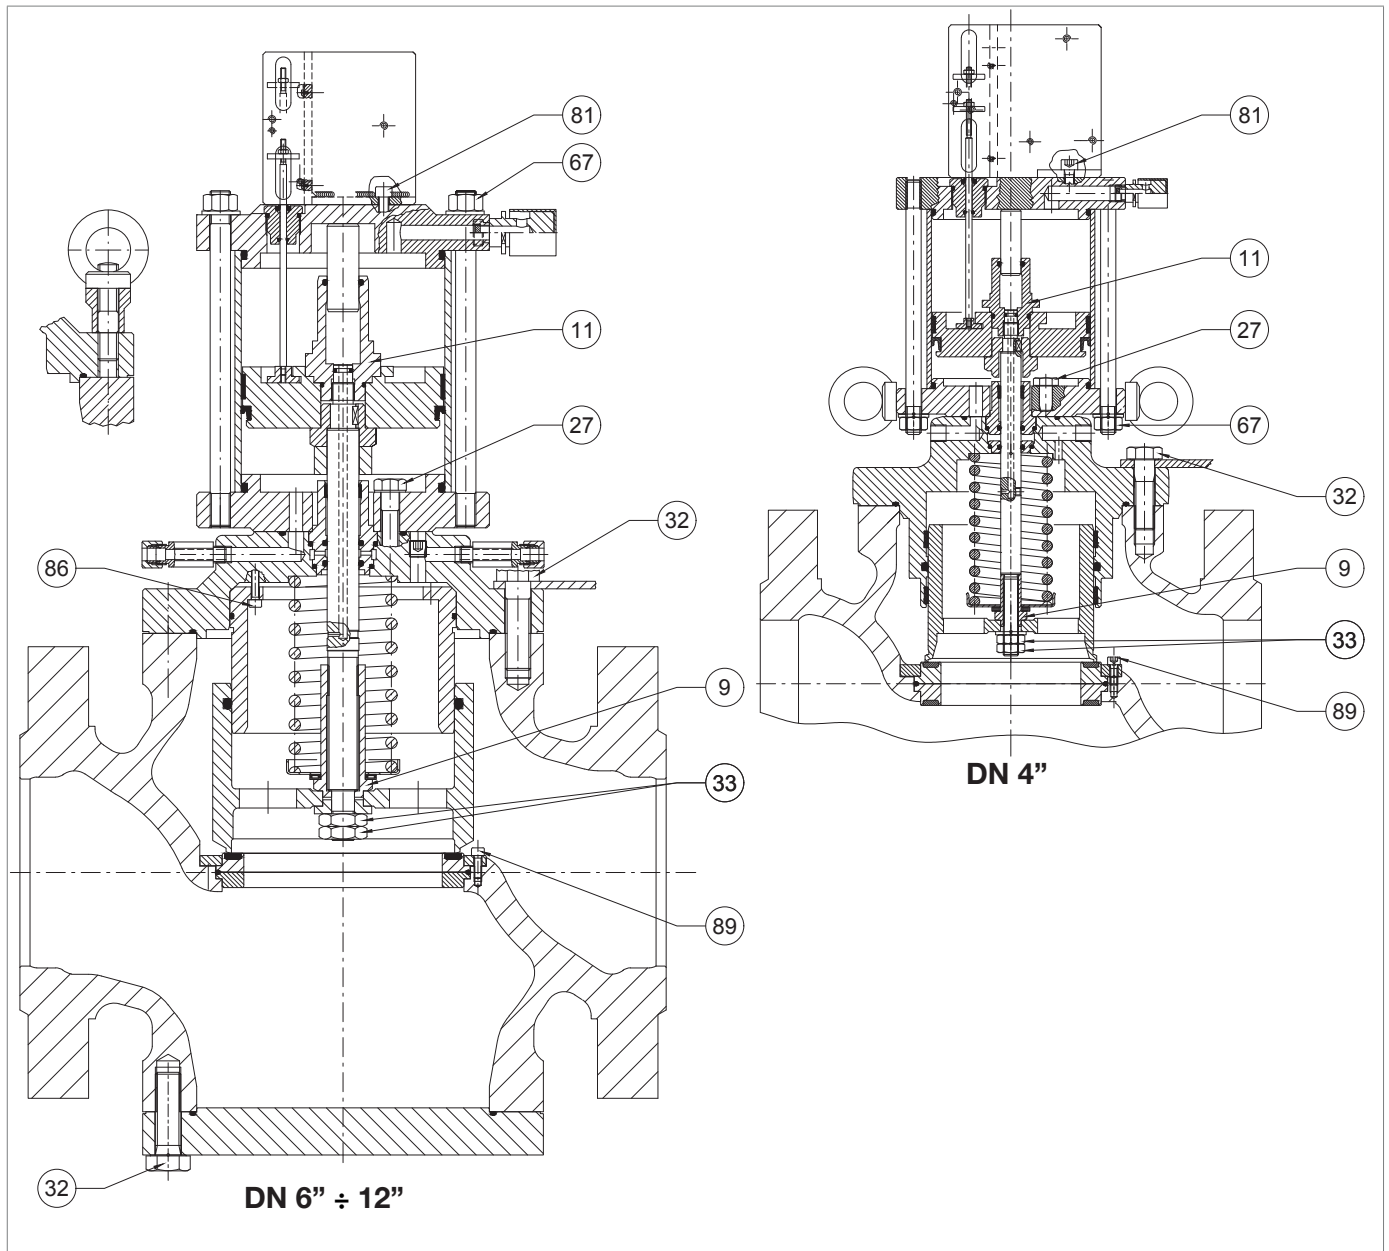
Coppie di serraggio valvola di blocco incorporata HBC 975
